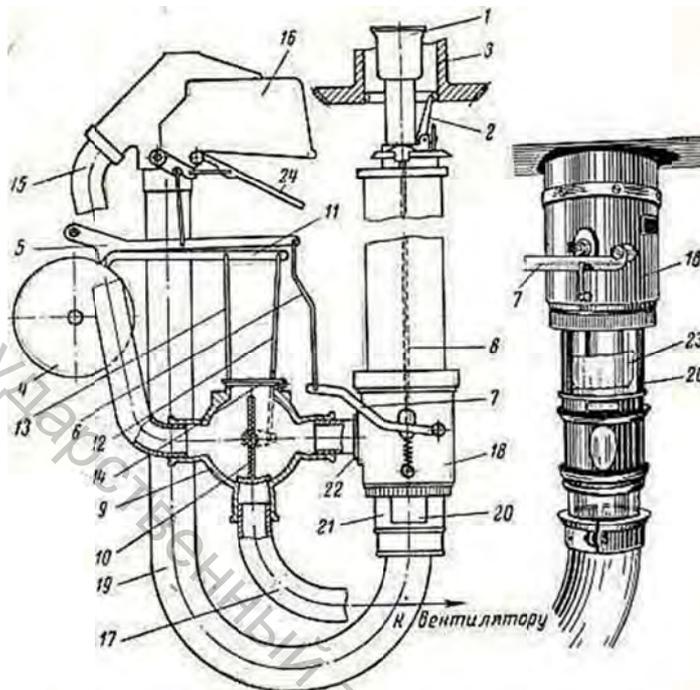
Механизм пневматической оттяжки с автоматической вывороткой изделия
